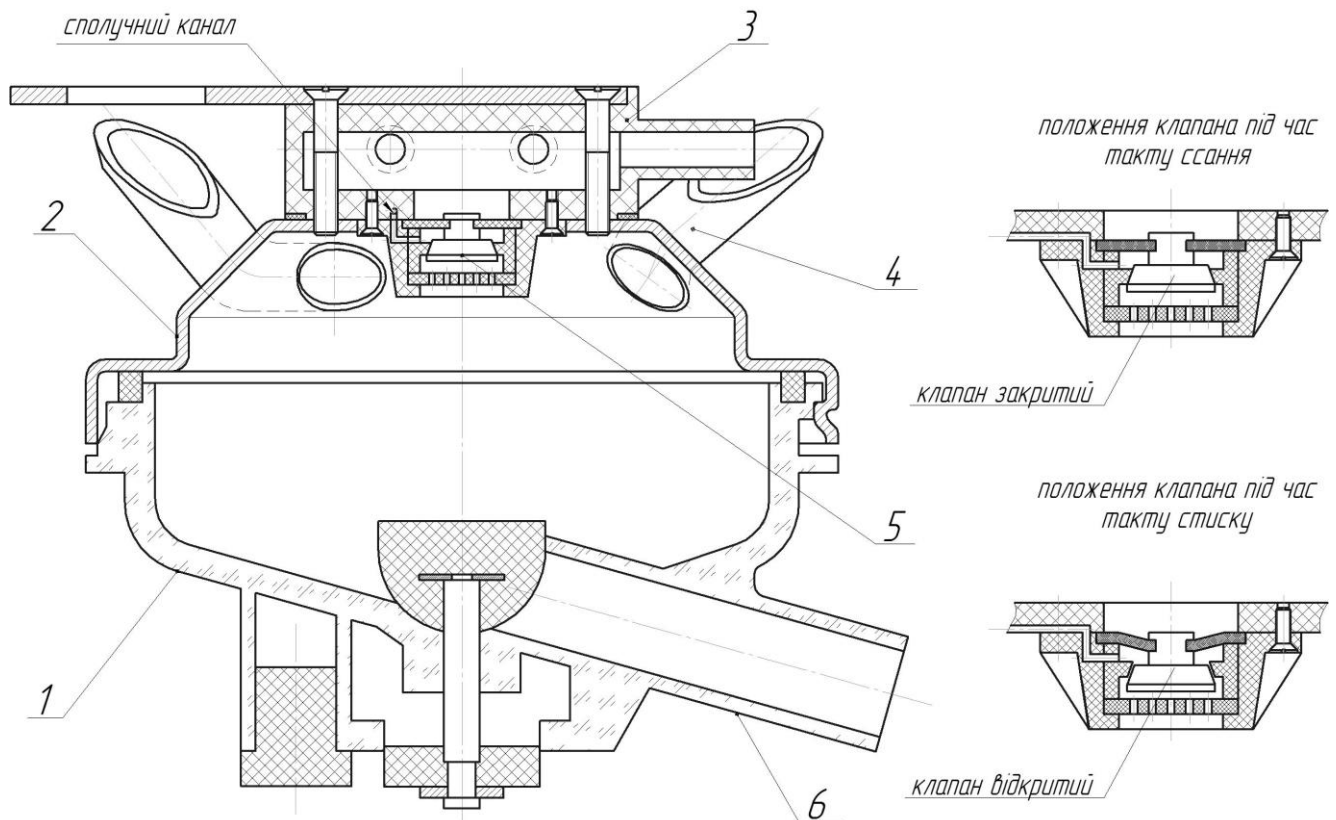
Удосконалений колектор доїльного апарата: 1 – корпус прозорий молокозбірної камери; 2 – корпус металевий; 3 – камера розподілу змінного тиску; 4 – патрубок з вигином молочної трубки; 5 – клапан з мембраною; 6 – відвідний патрубок молока
